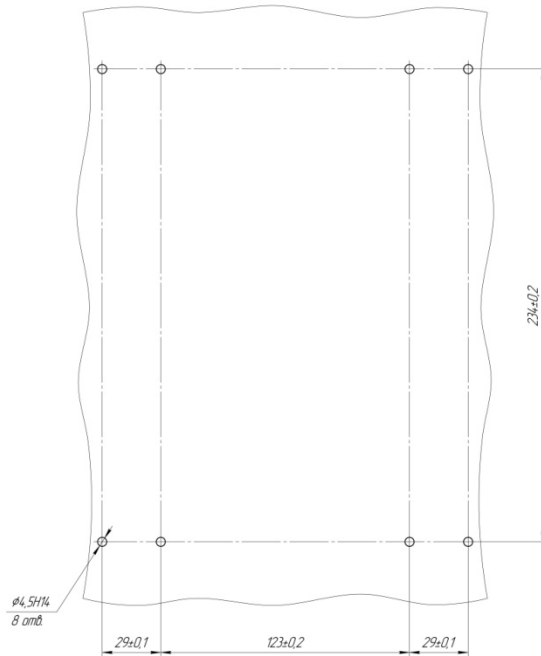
Габаритные и присоединительные размеры релейного блока РС830-ФПТ при внешнем монтаже, обеспечивающем его поворот вверх/вниз
